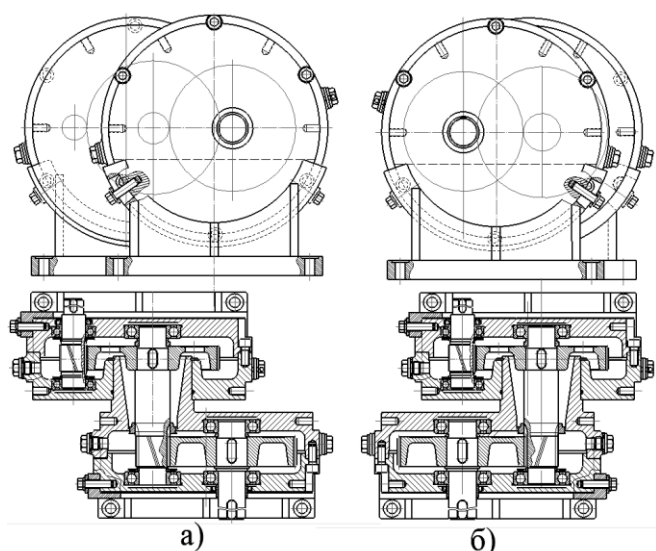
Преобразование развёрнутого редуктора (а) в соосный (б) за счёт поворота корпуса тихоходной ступени и его опоры на 180°
